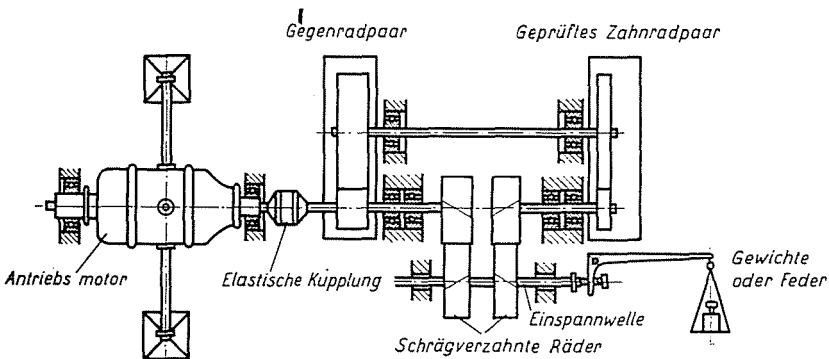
Dauerprüfmaschine mit geschlossenem Kraftverlauf. Ausführung: Lehrstuhl für Maschinenelemente
